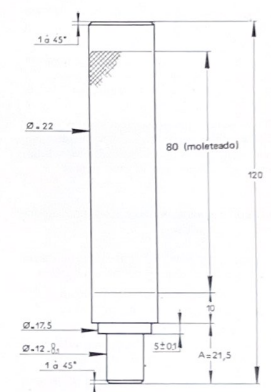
Mandril para la colocación del rodamiento de agujas en el mandrinado del cigüeñal.
